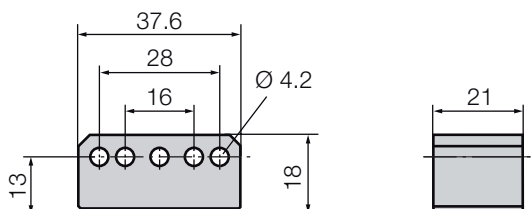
Dimensioni di ingombro datore di posizione BTL6-A-3801-2
